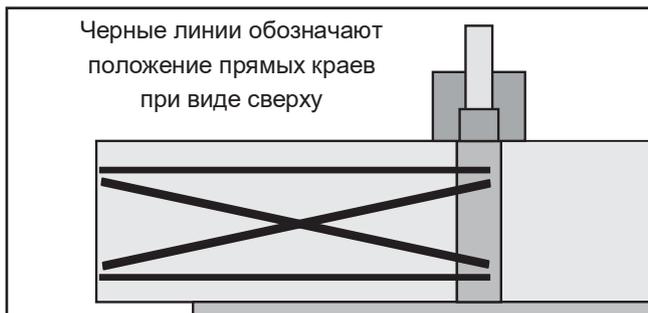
Положения прямых кромок для проверки параллельности подающего стола режущей головке.
